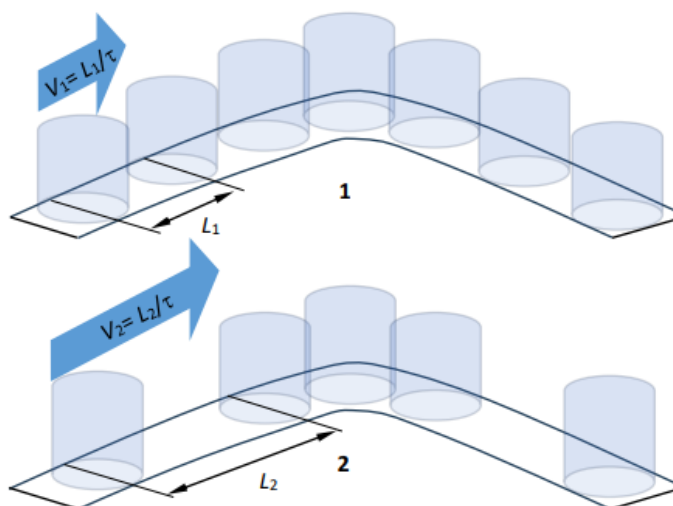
Схематичне пояснення впливу швидкості руху сопла на товщину надрукованого металу: 1 - мала швидкість руху сопла; 2 - висока швидкість руху сопла
